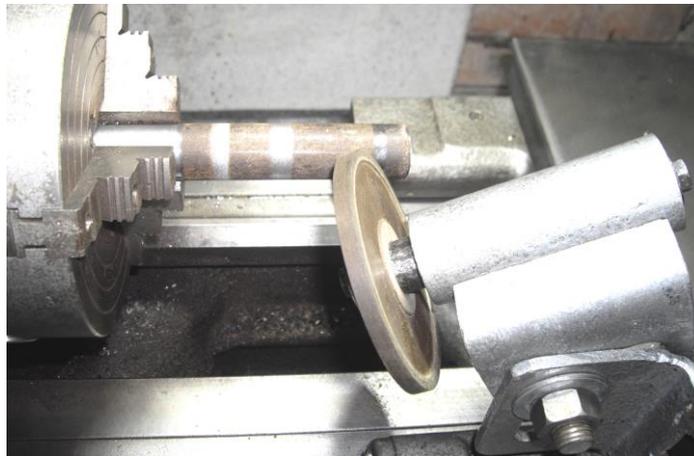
Використання шліфувальної головки, встановленої на токарному верстаті
